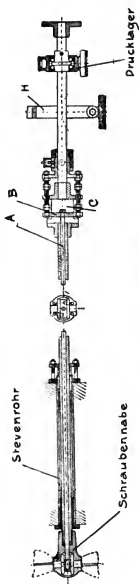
Wellenanlage mit einer Umsteuerschraube.
